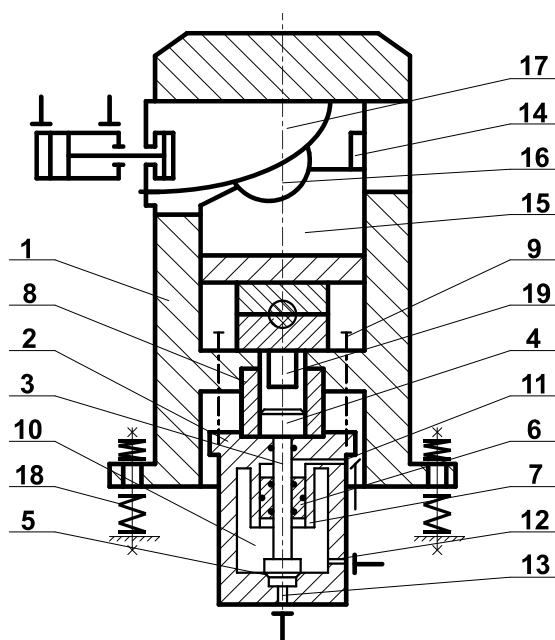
Конструктивная схема клиношарнирного пресс-молота [10]
